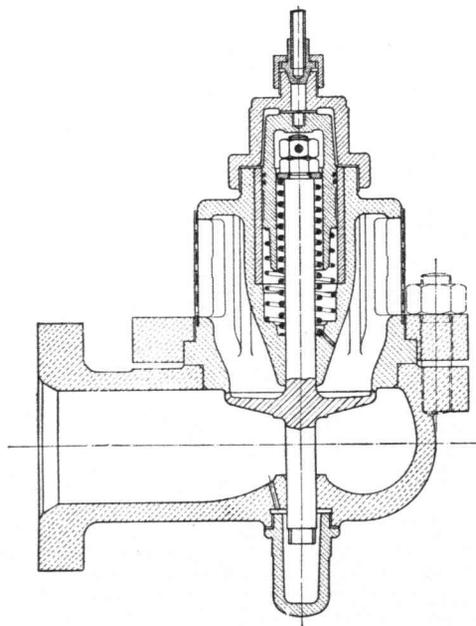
Durch Druckluft gesteuertes Luftsaugventil.
